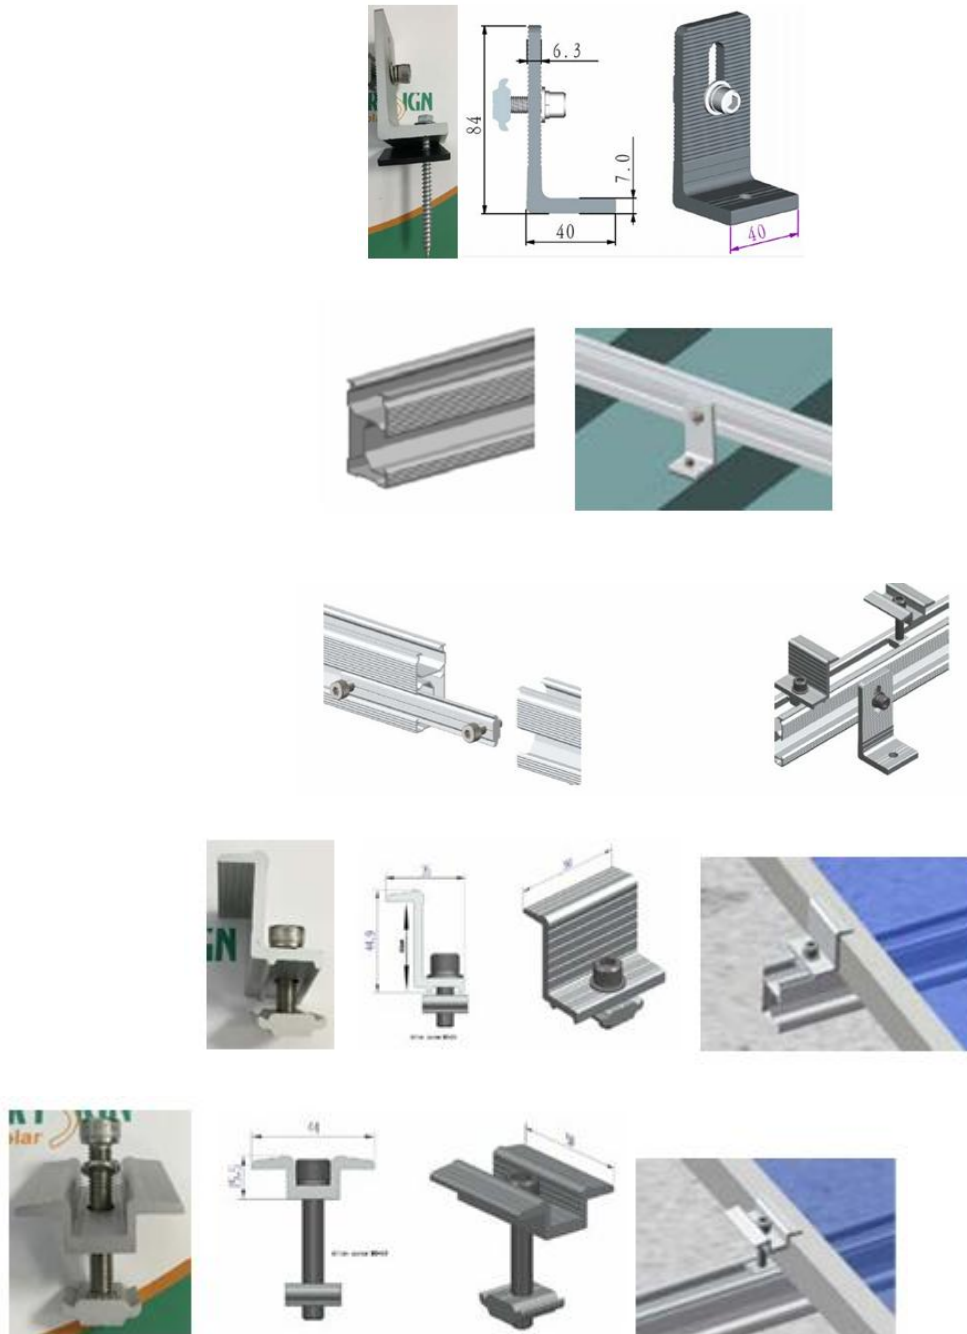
Disposición de las estructuras en alineación coplanar sobre la cubierta
